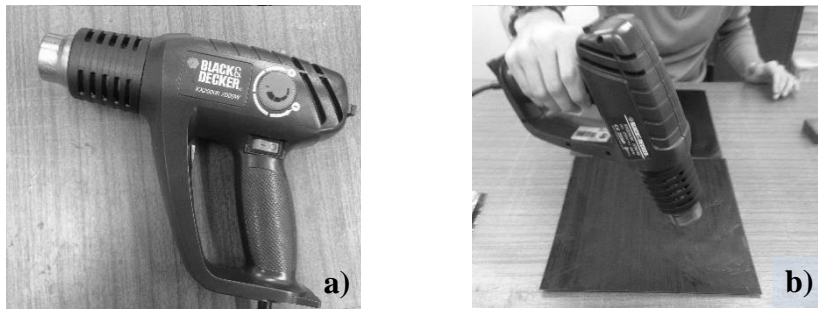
a) Pistola de ar quente; b) Aquecimento do pré-impregnado de carbono.
